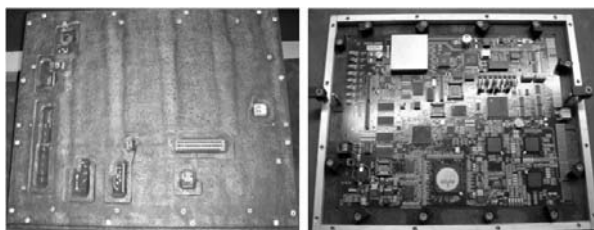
采用阻焊掩模板来保护 PCBA
